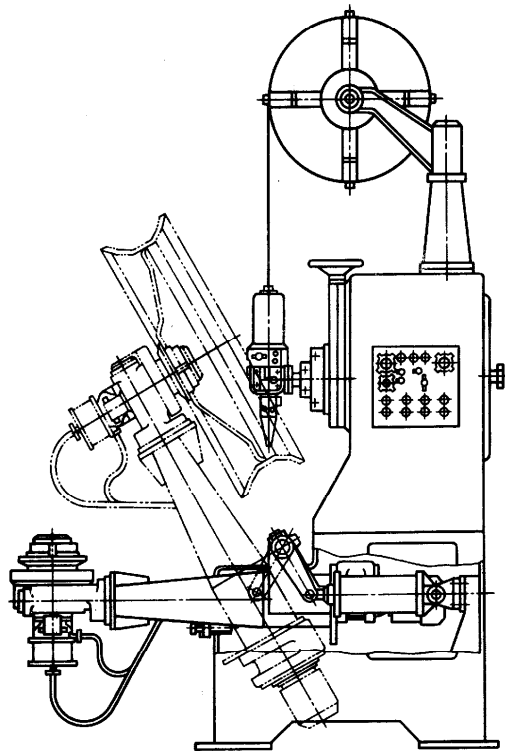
Конструкция автомата для сварки колес в положении «в лодочку»
